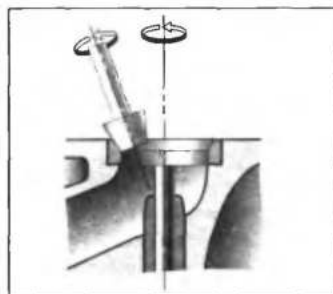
Схема эксцентричного шлифования седла клапана
